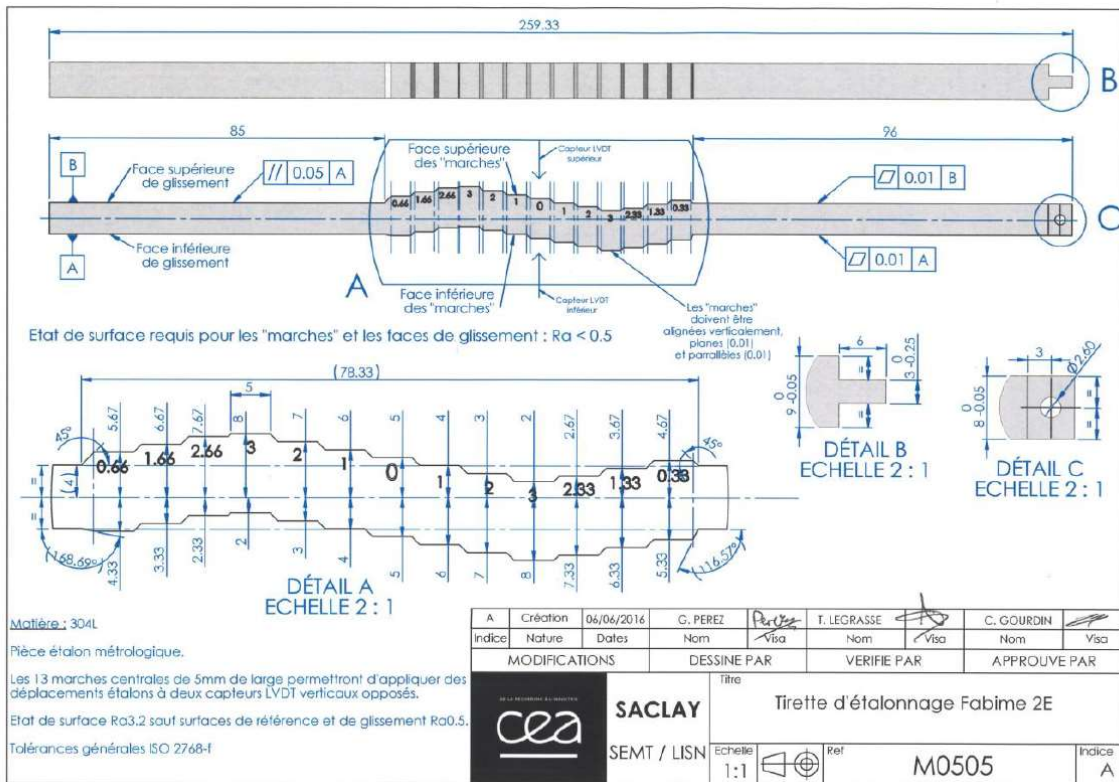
Plan détaillé de la tirette d'étalonnage pour FABIME2e
